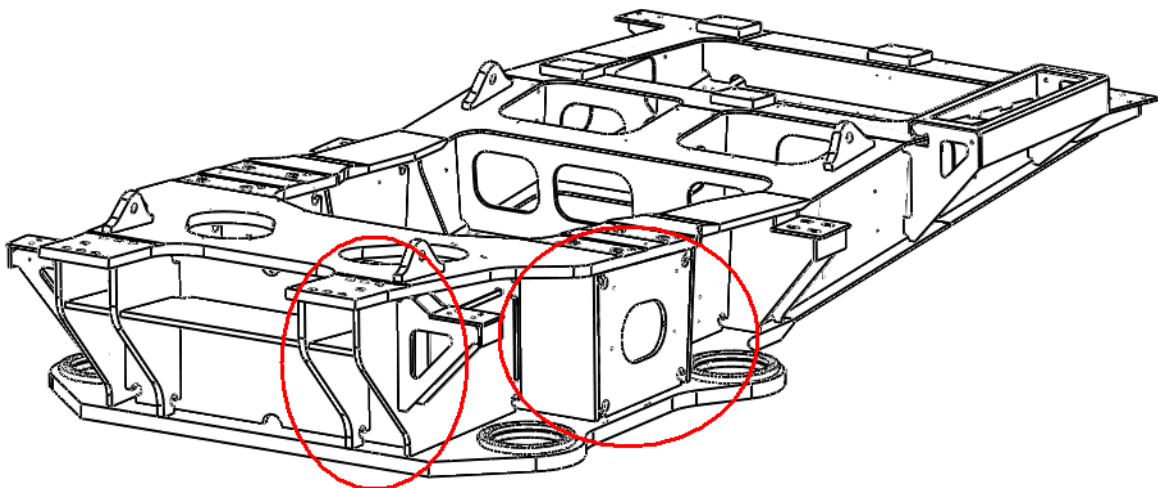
Hoch belastete Bereiche am Maschinenträger
